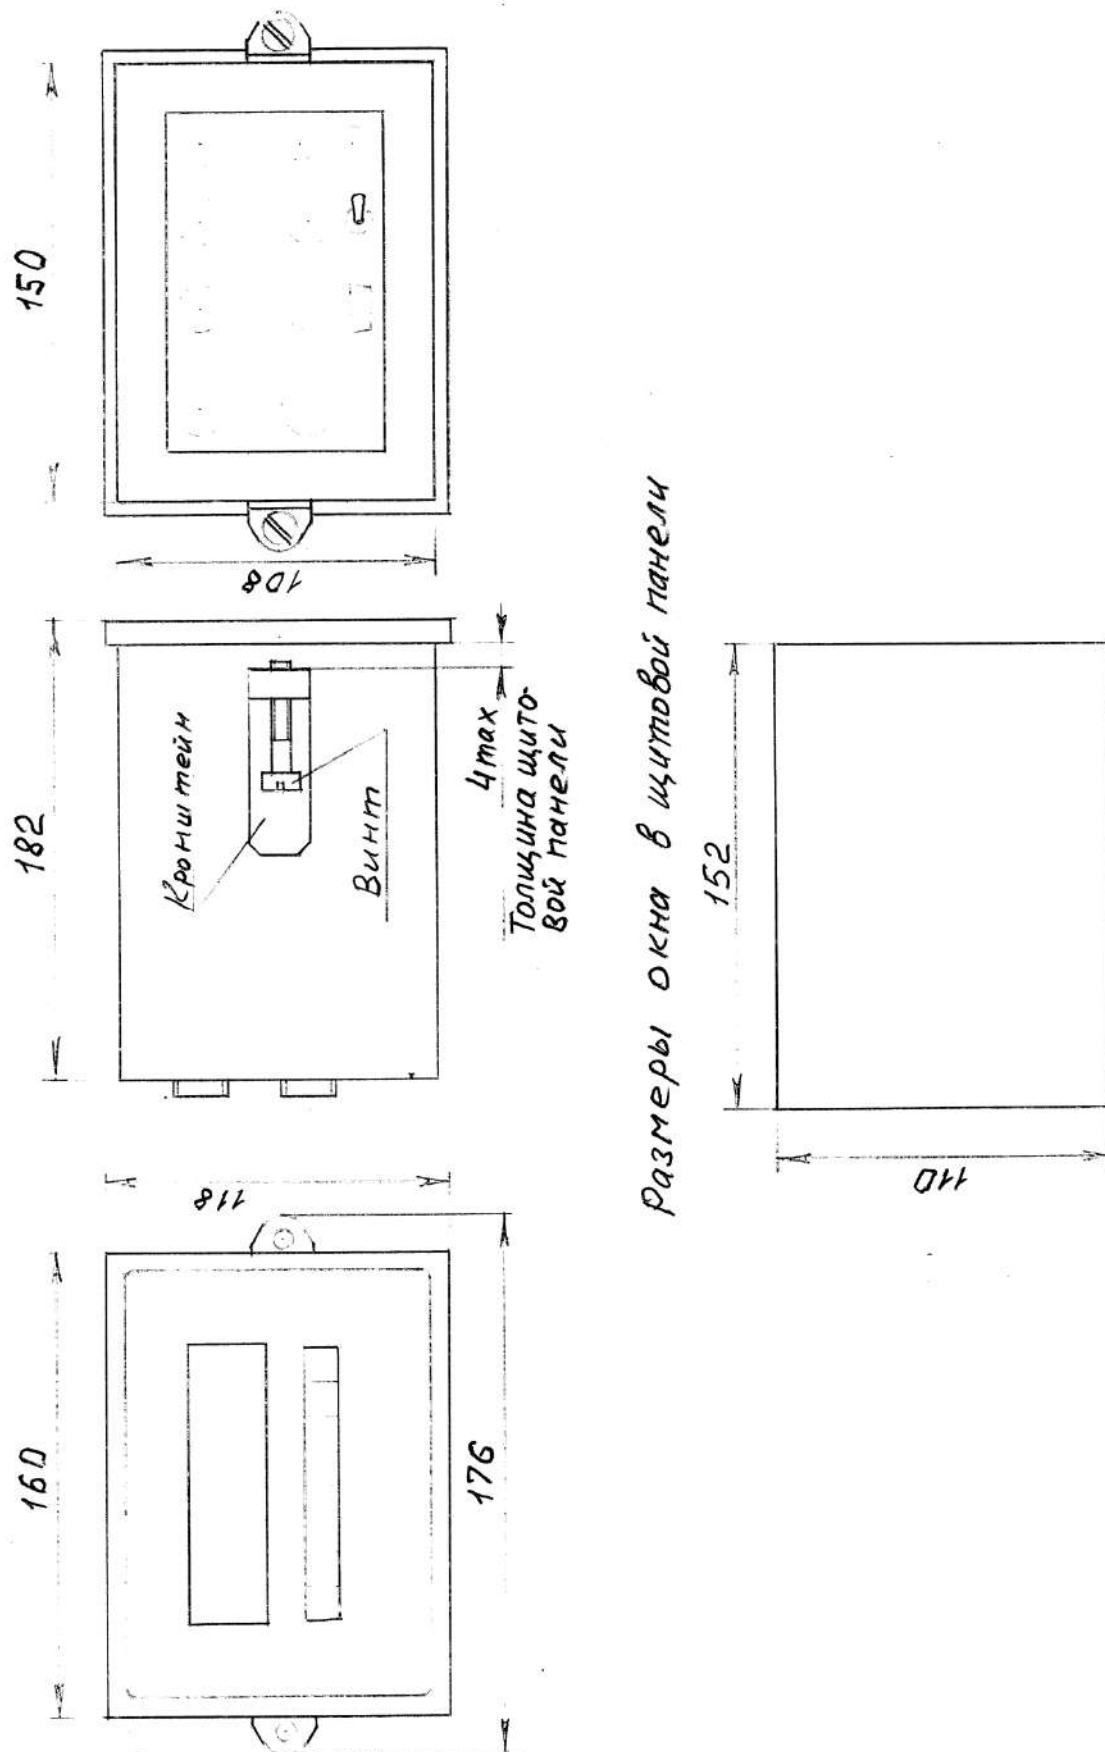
Габаритный чертёж измерительного блока и монтажного окна.
